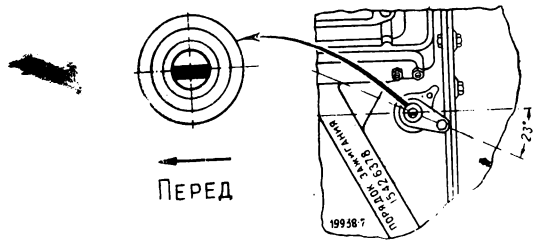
Установка коленчатого вала в положение в. м. т.: 1—метка; 2—указатель
